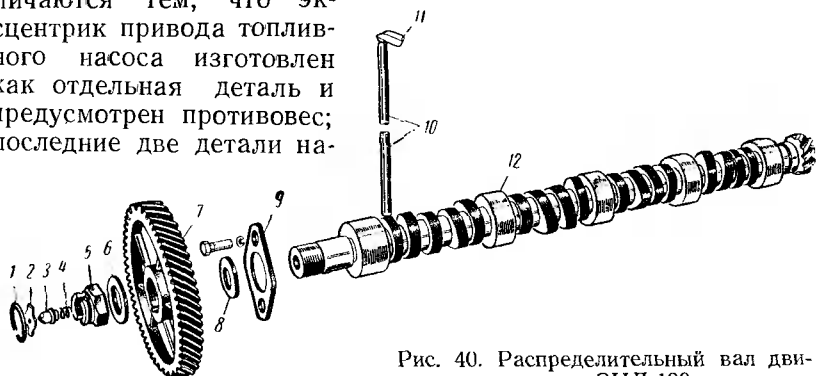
Распределительный вал двигателя ЗИЛ-130:
